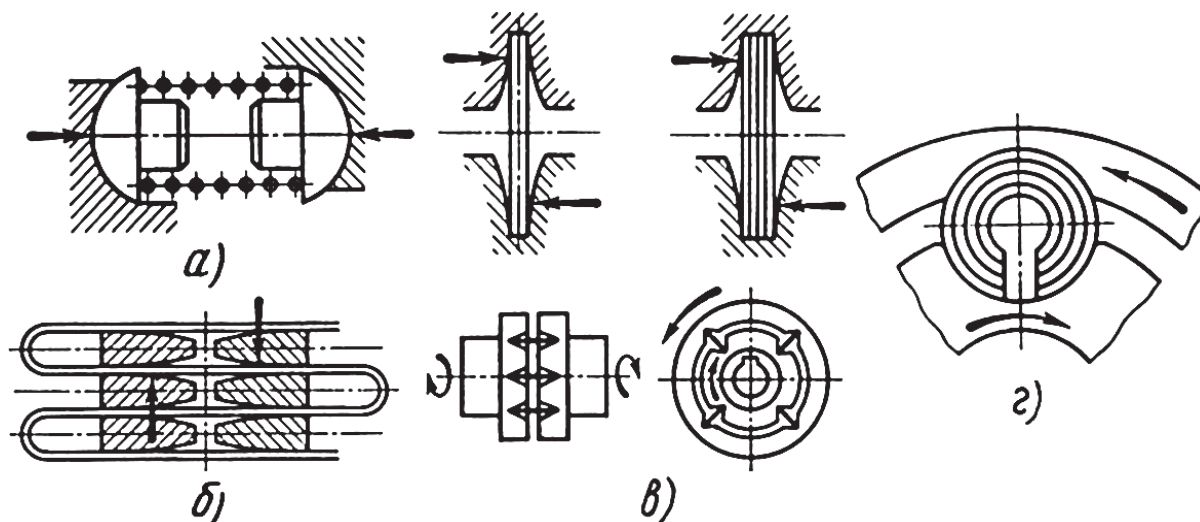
Основные типы металлических стальных упругих элементов муфт: а – цилиндрические пружины; б – змеевидные пластинчатые пружины; в – стержни, пластины и пакеты пластин, расположенные по образующей и по радиусу; г – пакеты разрезных гильзовых пружин
